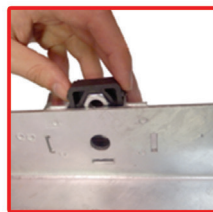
Сменный резьбовой блок - плавающий самоустанавливающийся блок крепления со сменной гайкой фиксации
